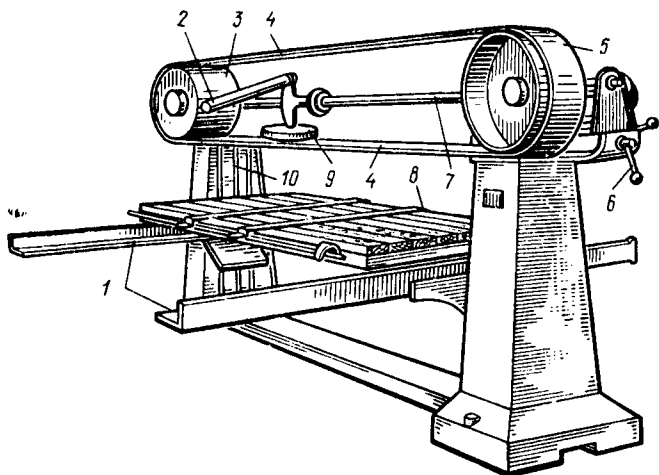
Шлифовальный ленточный станок ШЛПС-511
